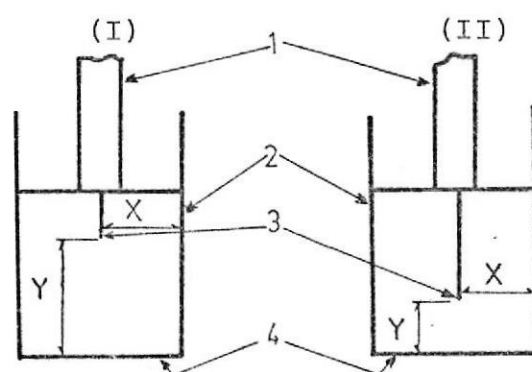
Representación del arreglo del extremo libre del electrodo para obtener un proceso de soldadura estable (Ref. 7).
